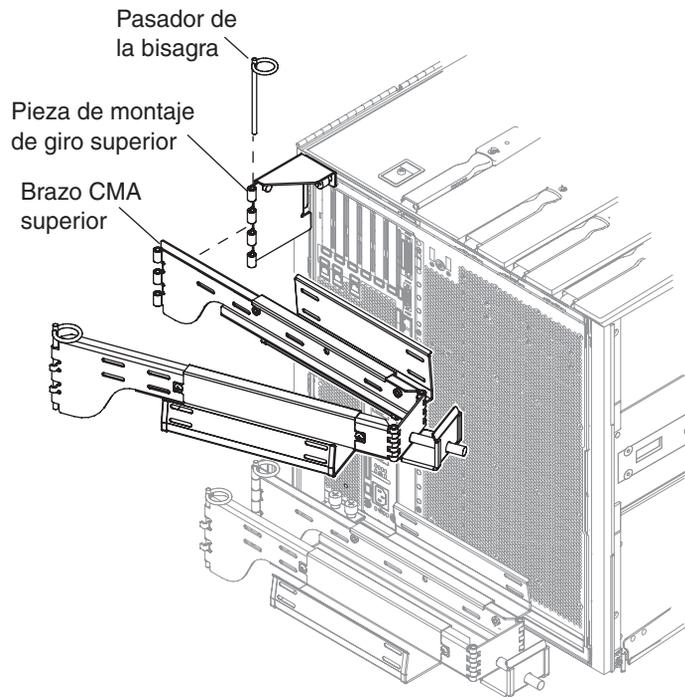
Montaje de la abrazadera CMA superior y la pieza de giro
